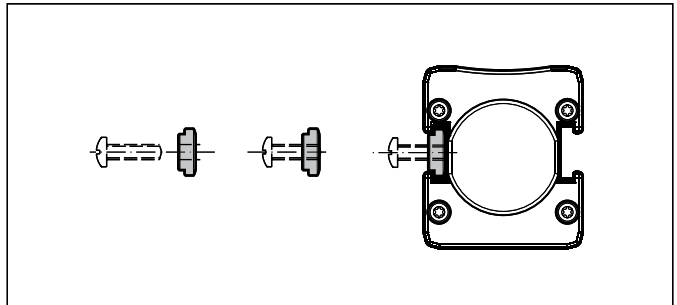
MONTAGE MIT BEFESTIGUNGSMUTTERN
